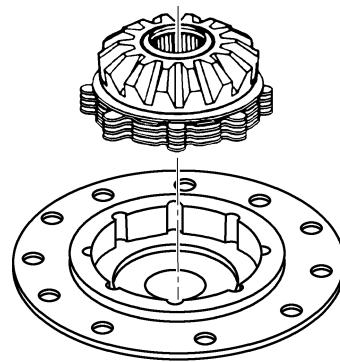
从右半壳拆卸半轴齿轮和离合器盘片组
